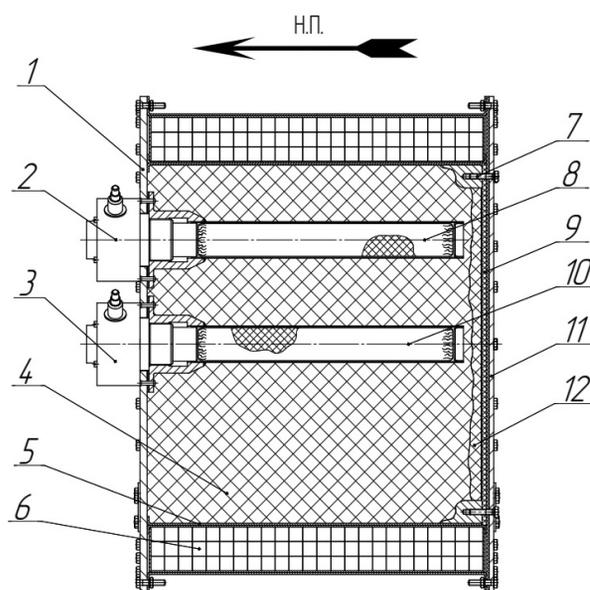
Предполагаемая конструктивно-компоновочная схема БЧ Е-600 (Н.П. — направление полёта ЗУР): 1, 11 — днища; 2, 3 — ПИМ (основной и дополнительный); 4 — РЗ (разрывной заряд); 5 — корпус; 6 — ГПЭ; 7 — болт; 8, 10 — дополнительный детонатор; 9 — прокладки; 12 — тротиловая «пробка»
